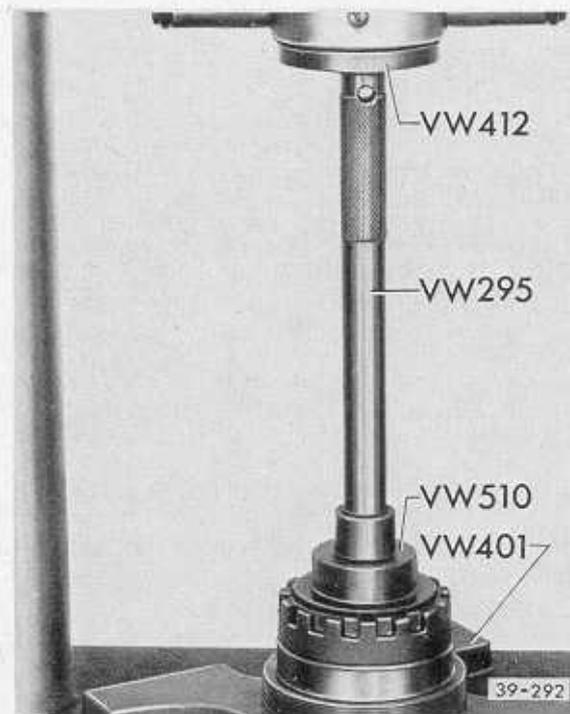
Außenring für Kegelrollenlager bis auf Anschlag einpressen.
